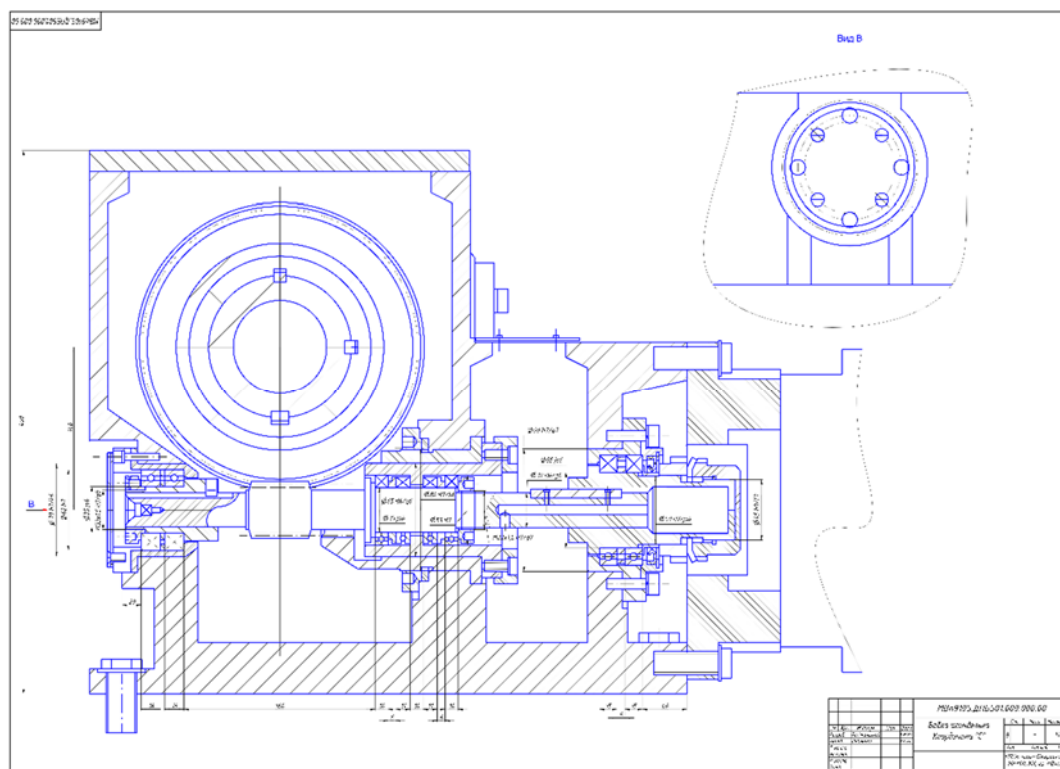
Кінематична схема приводу шпинделя базового верстату
